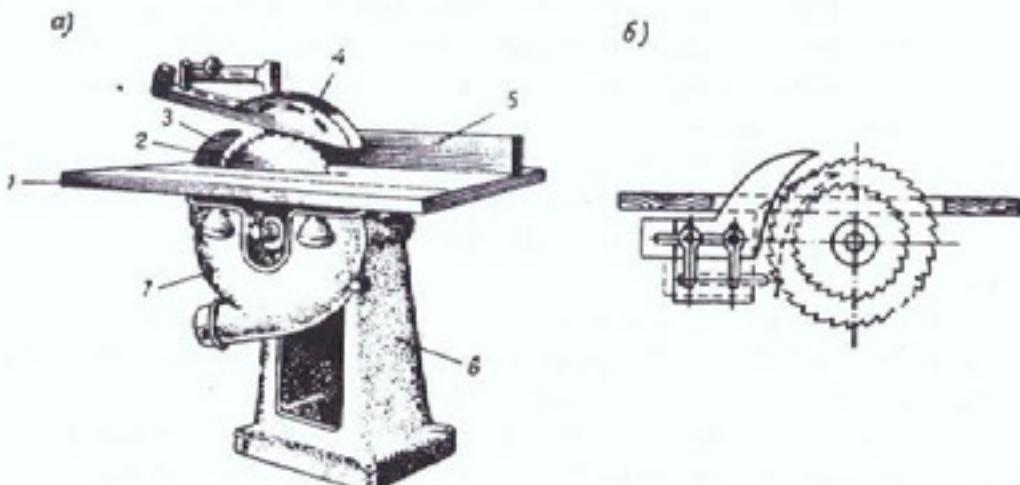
Круглопильный станок для продольного пиления с ручной подачей: а — общий вид; б — установка расклинивающего ножа.
